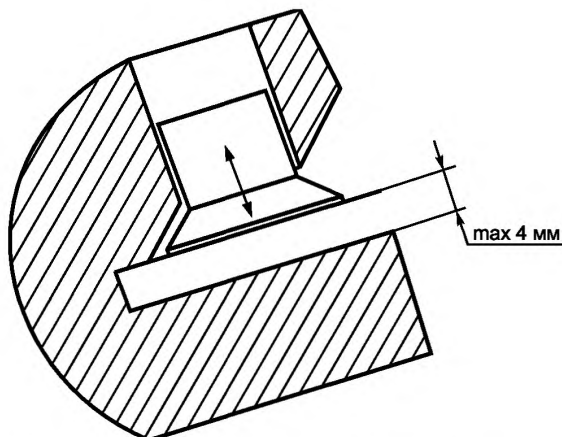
Пример линейного перемещения в устройстве для закрепления печатной формы
